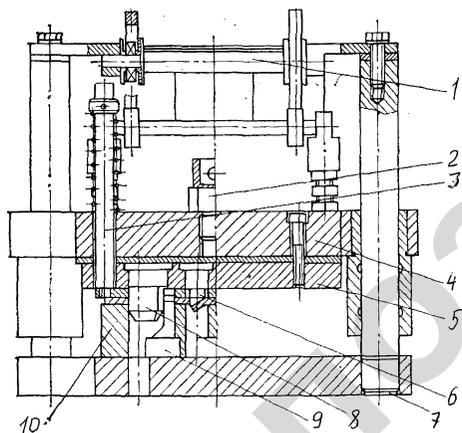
Схема штампа для восстановления планок цепи:
